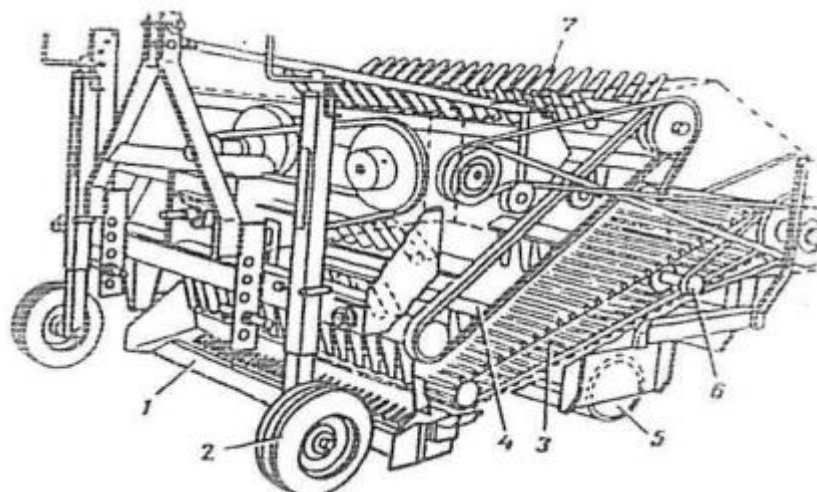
Копач-валкоукладач Vibro (Італія): 1 – ніж зубчастий; 2 – колеса опорні; 3 – елеватор; 4 – транспортер; 5 – ложеутворювач; 6 – струшувач; 7 – пальці обгумовані [5].
